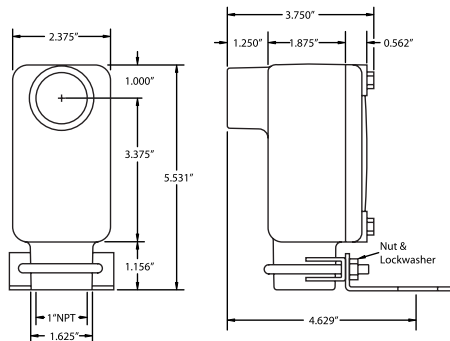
Dimensiones del sensor estándar 907 a prueba de explosiones
